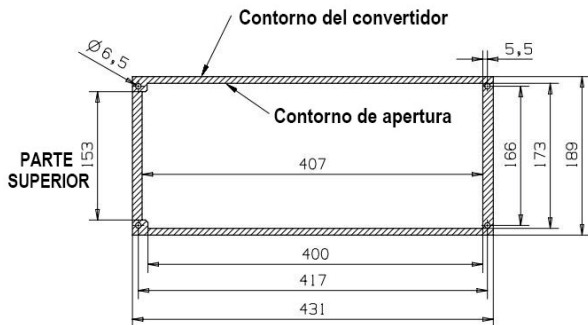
Dimensiones de corte del montaje con bridas para M15 (Unidad: mm)
